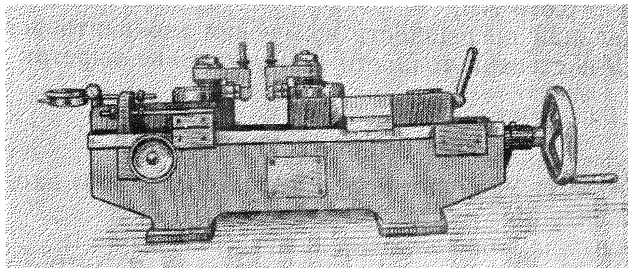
Межцентромер с кронштейнами для проверки малых колес
